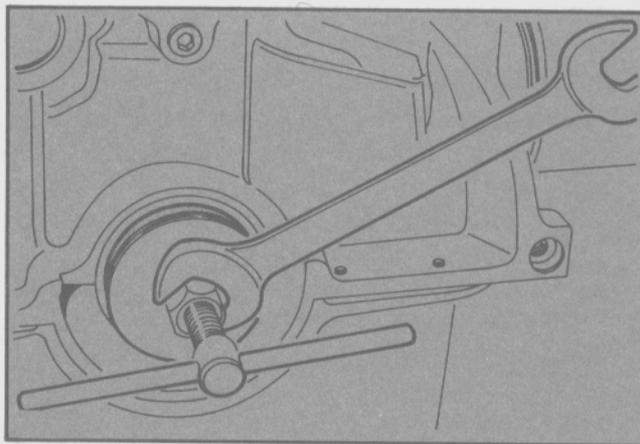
Desmontaje del retén trasero del cigüeñal
